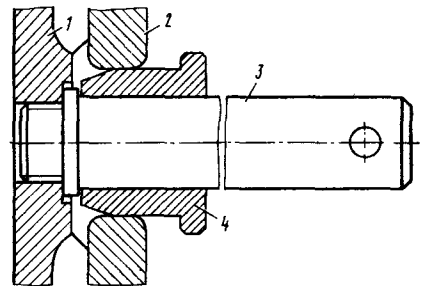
Приспособление для центровки рубашки при посадке ее на втулку цилиндра дизеля типа Д100: 1 — втулка; 2 — рубашка; 3 — стержень с резьбой; 4 — центрирующая втулка
